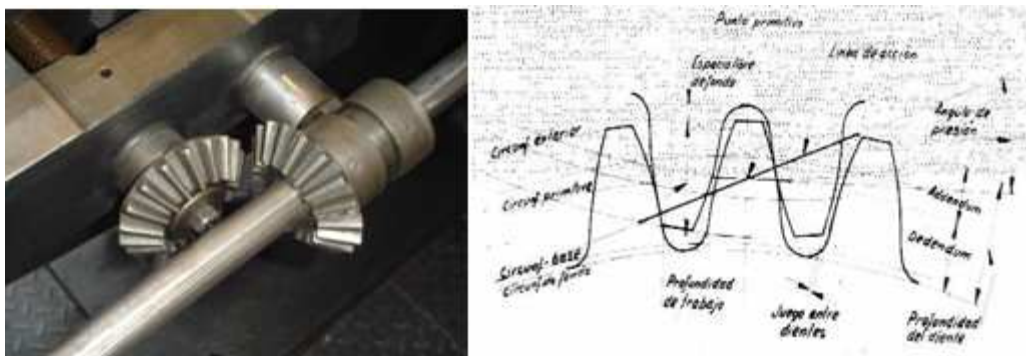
Sistema de Transmisión por Engranajes Cónicos
